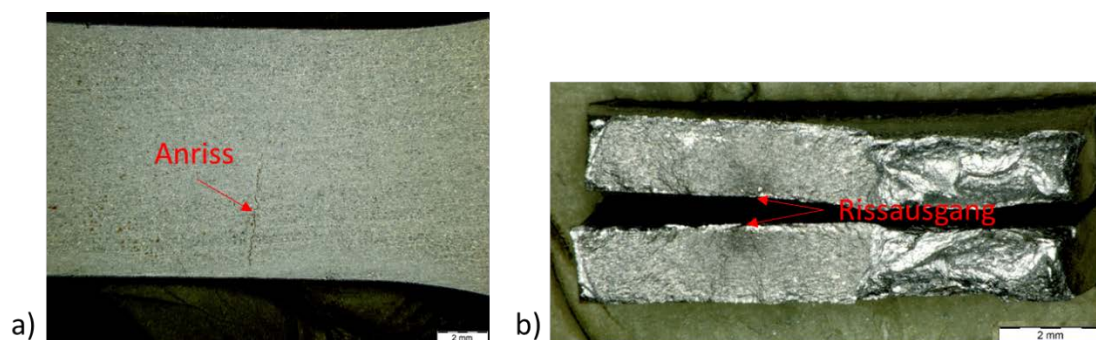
Rissausgangsort Walzoberfläche bei einer ungekerbten Flachprobe aus DC04 mit polierten Kanten, a) Draufsicht Walzoberfläche, b) Bruchflächen
